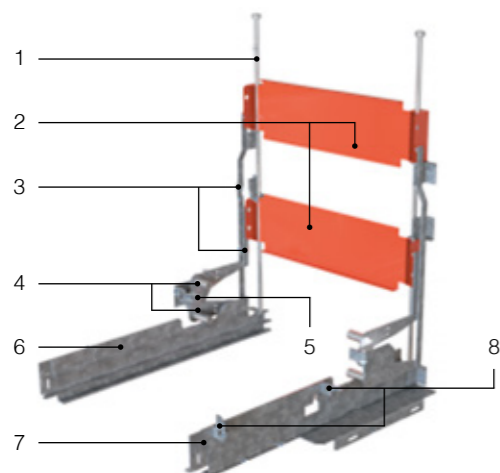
Устройство шторочного механизма с направляющими полозьями
